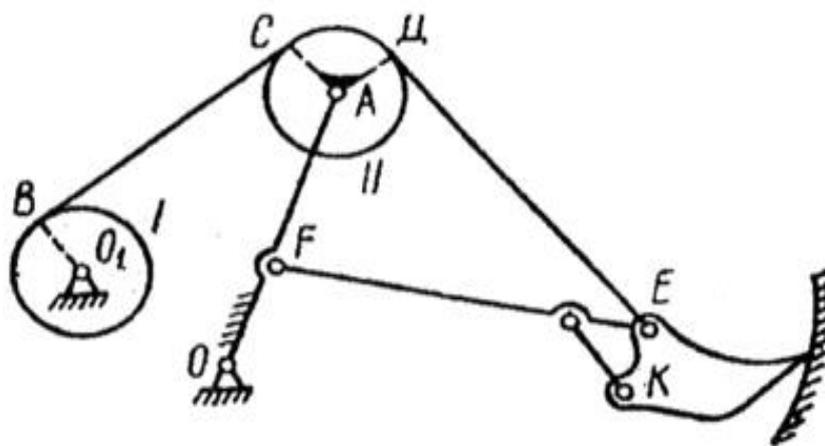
Кинематическая схема «механизма прямой лопаты» экскаватора
